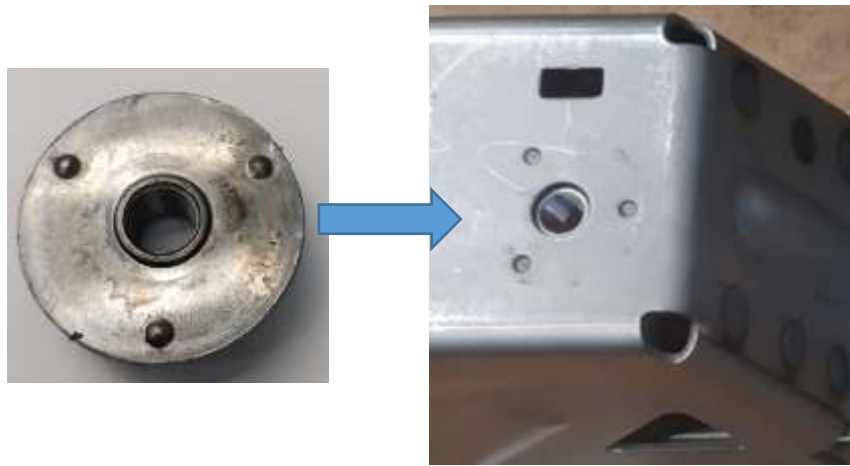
Exemplo de modificação efetuada a um componente sujeito a soldadura por protuberâncias de modo a otimizar a superfície de contacto entre a chapa e o componente.
